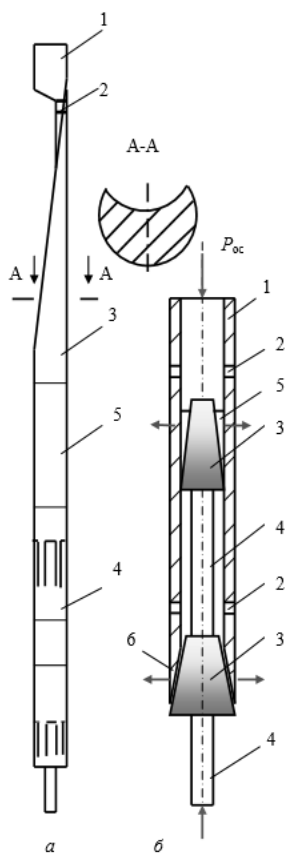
Схема компоновки стационарного клина КОС (а) и распорного механизма клина КОС (б)
